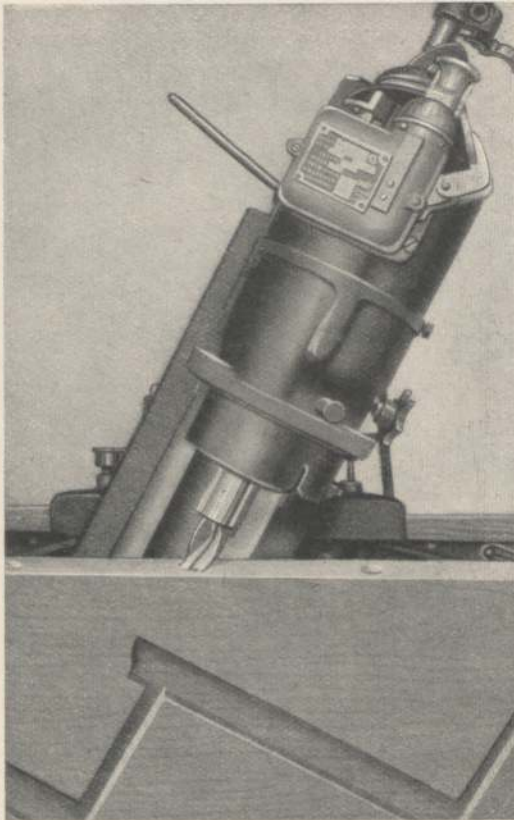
Die „Ruga“-Maschine (mit Ansicht des Motors) zum Bohren der Staketenlöcher einer Wange eingestellt.
